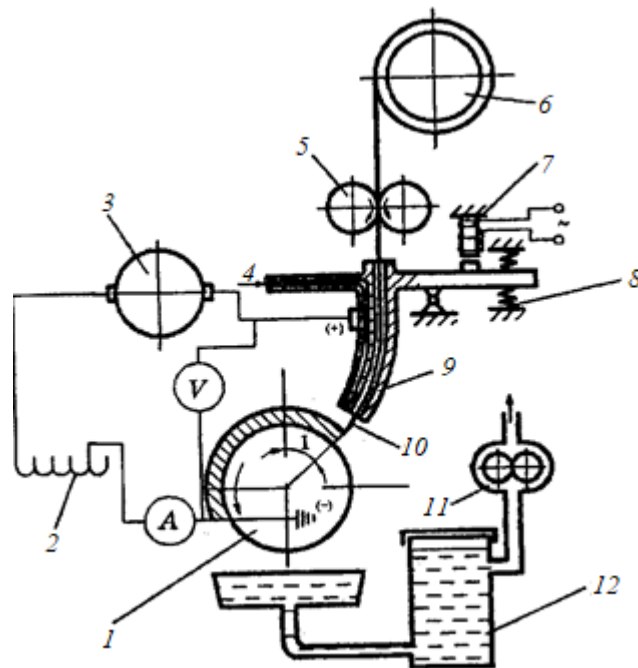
Схема установки для вібродугового наплавлення деталей
